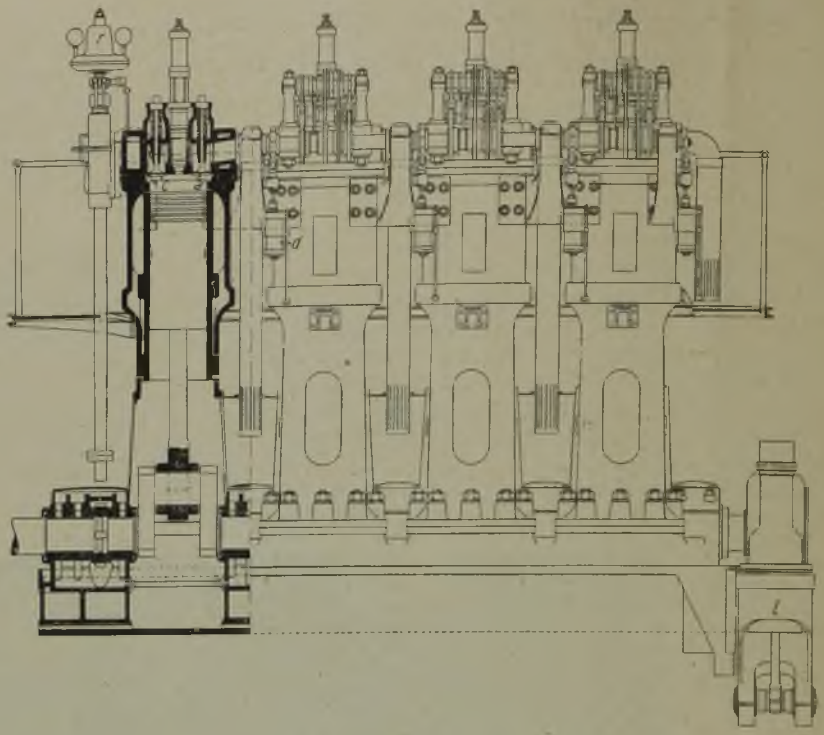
Vorderansicht des Dieselmotors und Schnitt durch einen Zylinder.]
